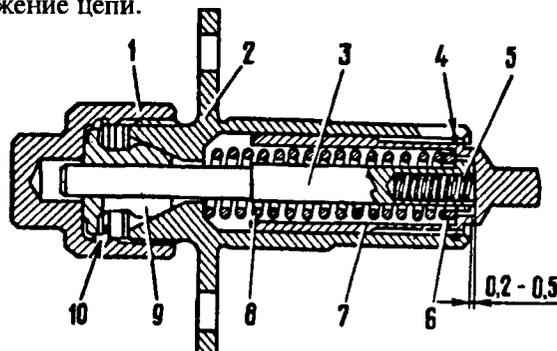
Разрез натяжителя цепи: 1 - колпачковая гайка; 2 - корпус натяжителя; 3 - стержень; 4 - пружинное кольцо; 5 - пружина плунжера; 6 - шайба; 7 - плунжер; 8 - пружина; 9 - сухарь; 10 - пружинное кольцо
